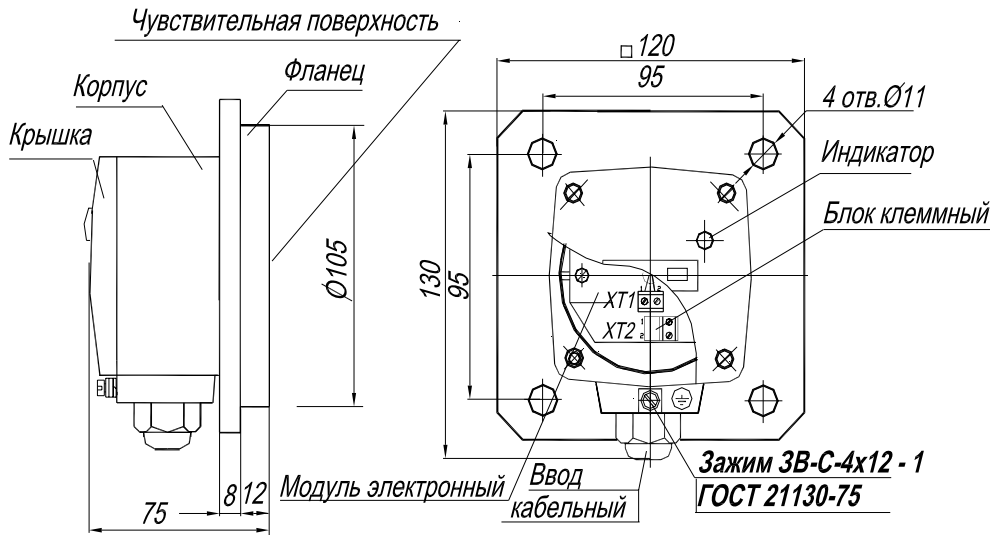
Внешний вид и габаритные размеры датчика
